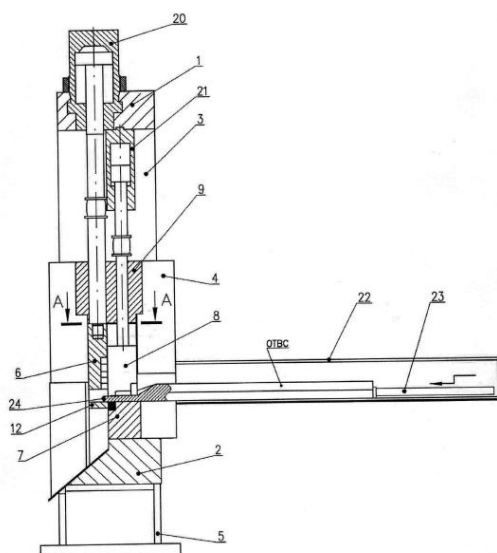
Установка для резки ОТВС: 6 – подвижный нож, 7 – неподвижный нож, 8 – прижим.
